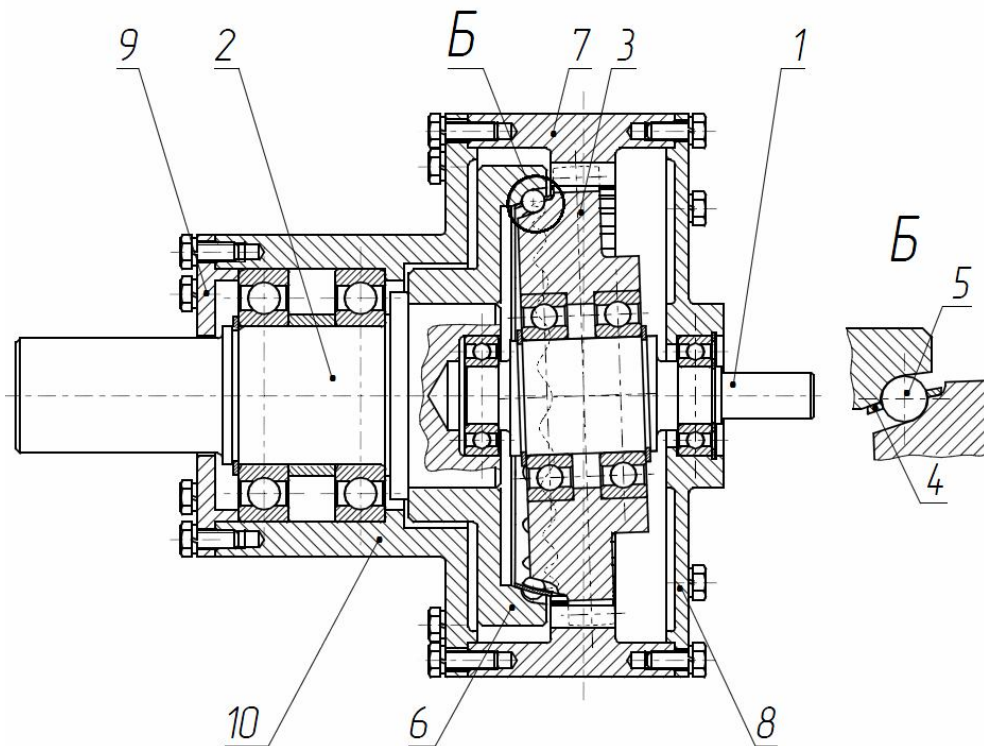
Конструкция одноступенчатой ВППТК с невращающимся прецессионным колесом: 1 – входной вал, 2 – выходной вал, 3 – прецессионное колесо, 4 – сепаратор, 5 – шарики, 6 – промежуточное колесо, 7 – корпус, 8 – крышка, 9 – крышка, 10 – стакан
